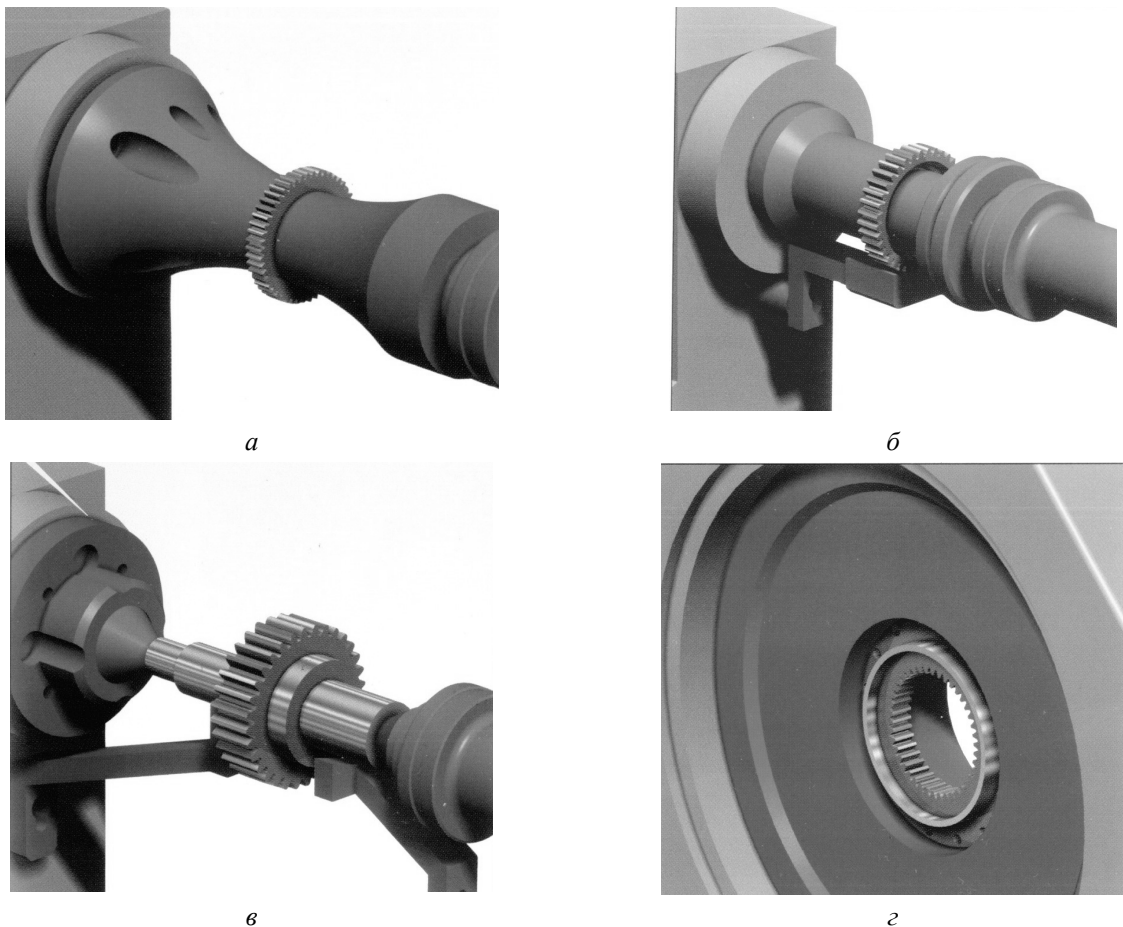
Закріплення деталей під час зубохонінгування: а – закріплення заготовки шестерні на оправці з натягом; б – оброблення в центрах з підтримкою; в – закріплення заготовки на спеціальній оправці для автоматичної заміни деталі; г – закріплення обробного зубчастого колеса для хонінгування внутрішніх зубців
